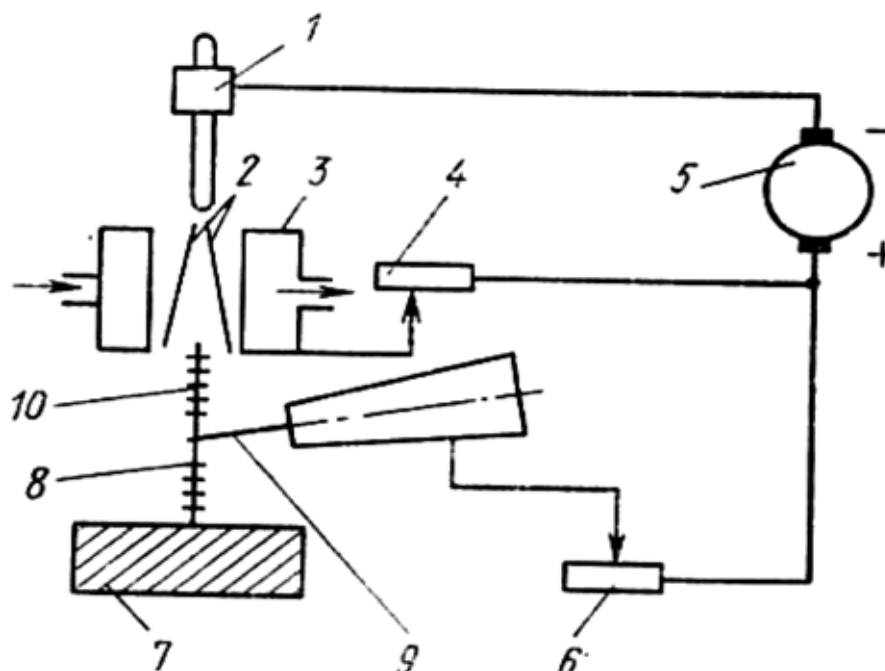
Схема установки для плазменной наплавки проволокой или стержнем: 1 — вольфрамовый электрод; 2 — плазмообразующий газ; 3 — сопло плазмотрона; 4 — электросопротивление; 5 — источник электропитания; 6 — балластное электрическое сопротивление; 7 — восстанавливаемая деталь; 8 — плазменный факел; 9 — присадочная проволока; 10 — плазменная струя
